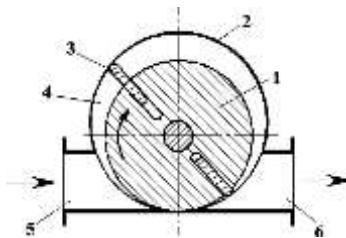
Схема пластинчастого ротаційного насоса: 1 – ротор; 2 – корпус; 3 – пластини; 4 – робочий простір; 5 – всмоктувальний патрубок; 6 – нагнітальний патрубок
